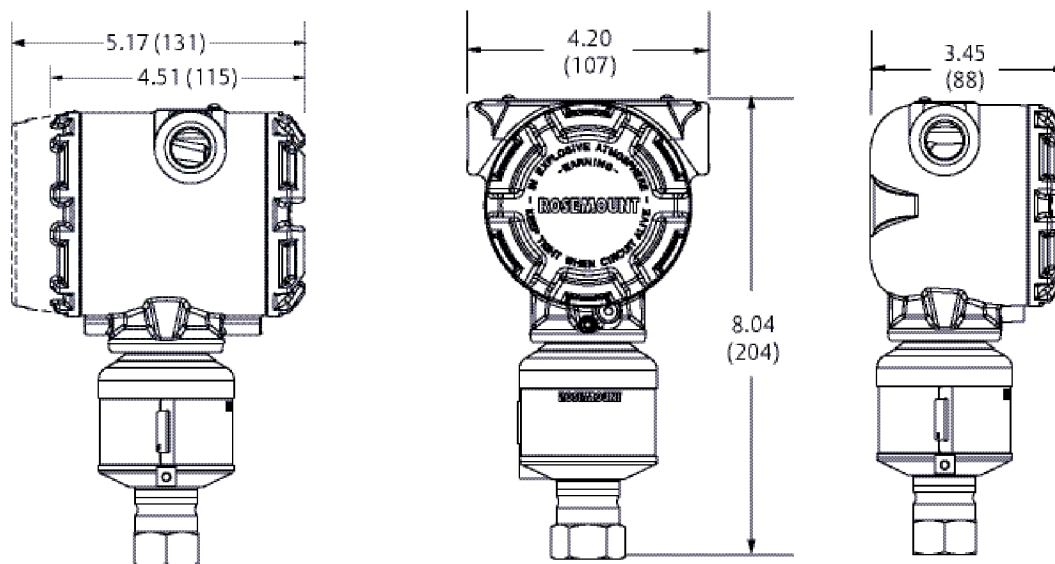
Rosemount Messumformer 3051S für ERS-Messungen in Coplanar Ausführung
